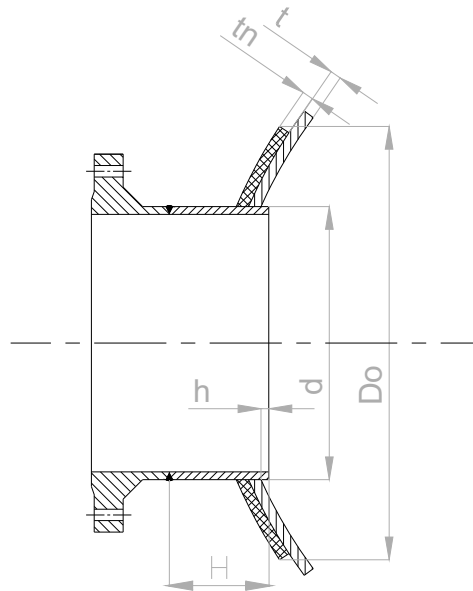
Esquema de las dimensiones más relevantes para el cálculo del refuerzo de la abertura⁶⁷
